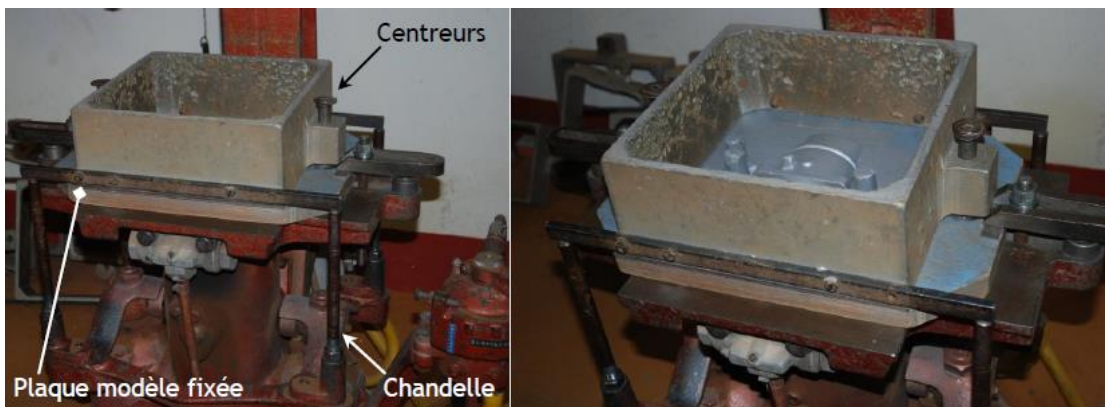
Plaque modèle fixée sur la machine et le châssis positionné.
